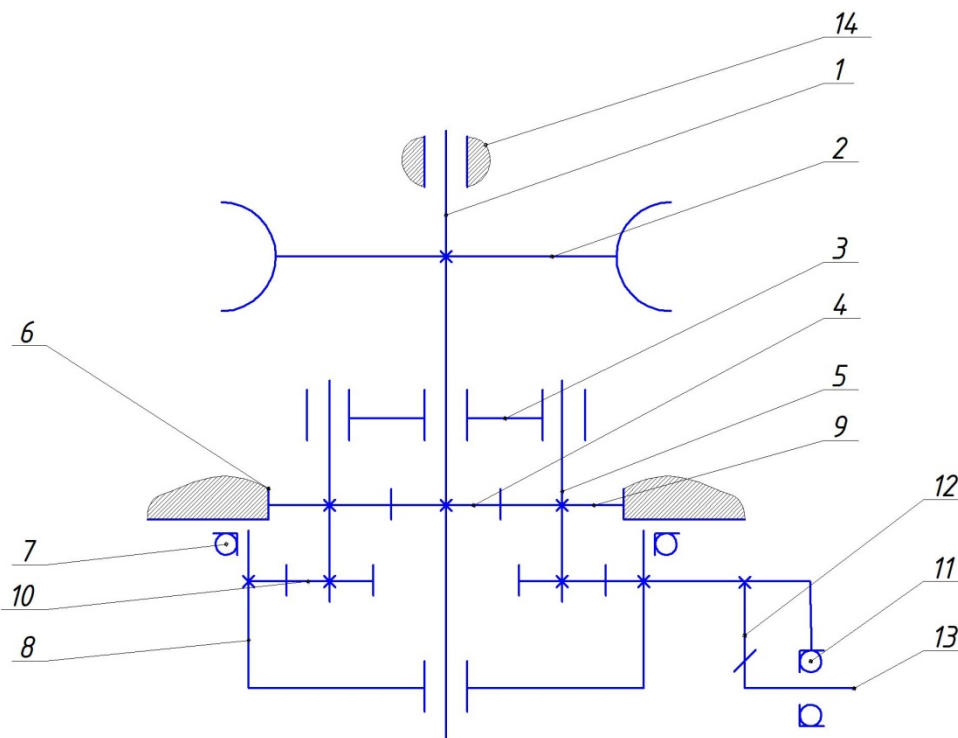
Кінематична схема ротаційної мийної головки: 1 – вал; 2 – турбіна; 3 – водило; 4 – сонячна шестірня; 5 – вісь сателіта; 6 – внутрішній вінець; 7, 11 – підшипники; 8 – рухома частина корпусу головки; 9 – сателітна шестірня; 10 – нижня сателітна шестірня; 12 – конічна шестірня; 13 – вісь форсунок; 14 – корпус ротаційної головки.
